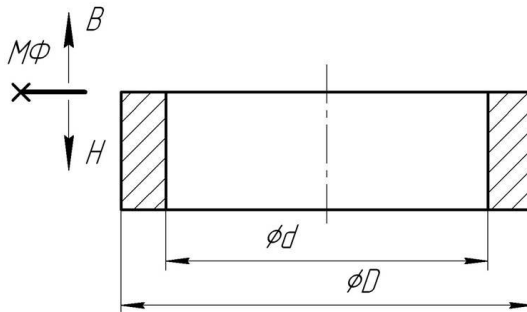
Положення площини рознімання для лиття підшипника в піщаній формі
